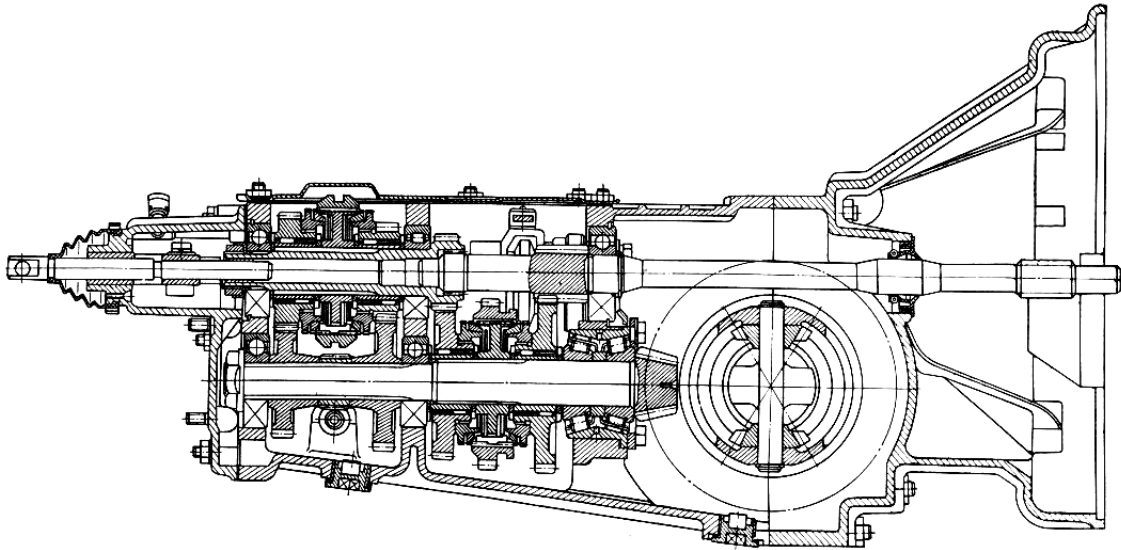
Конструкция коробки передач автомобиля ЗАЗ-968
